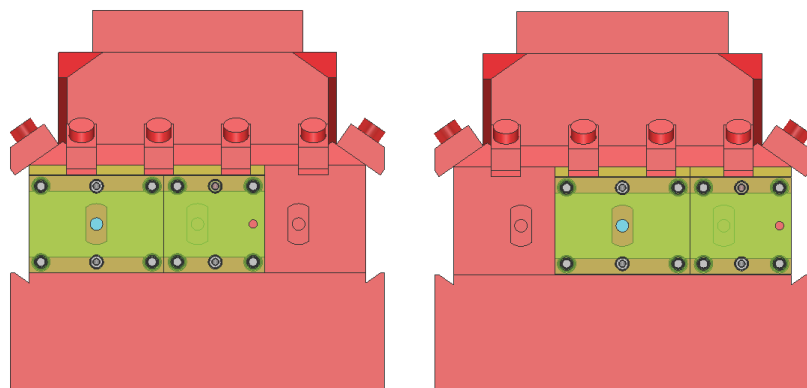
Příklad rozvedení chladicí kapaliny revolverovou hlavou Sauter[21]
